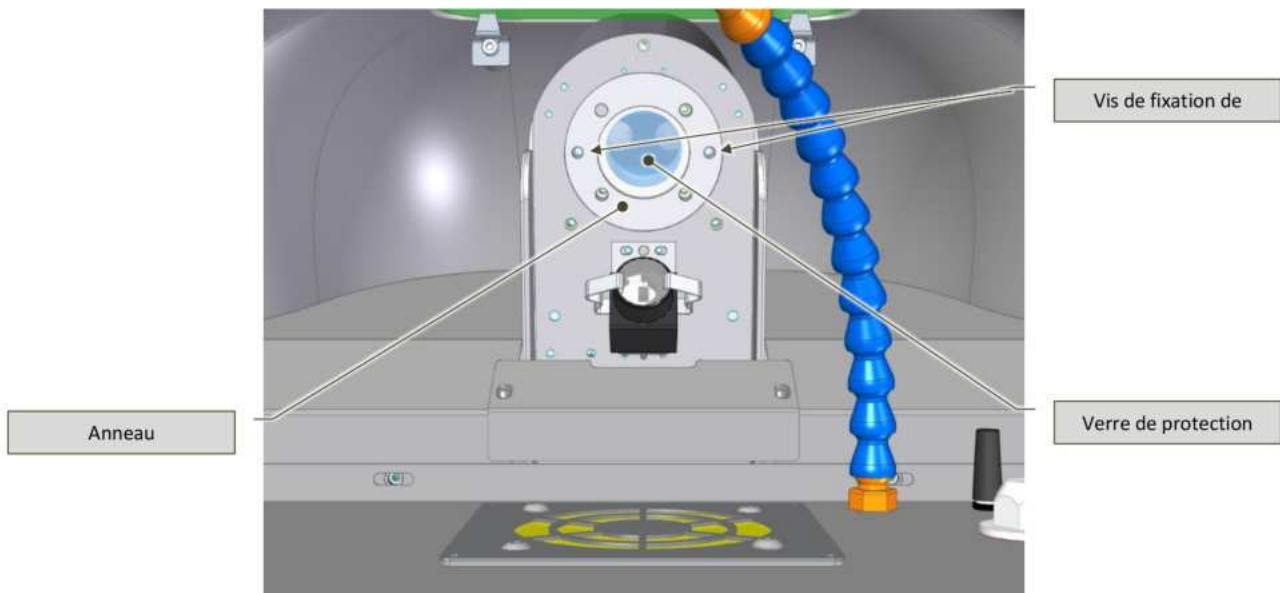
Remplacement du verre de protection spécial – vue de bas en haut de la chambre de soudage
